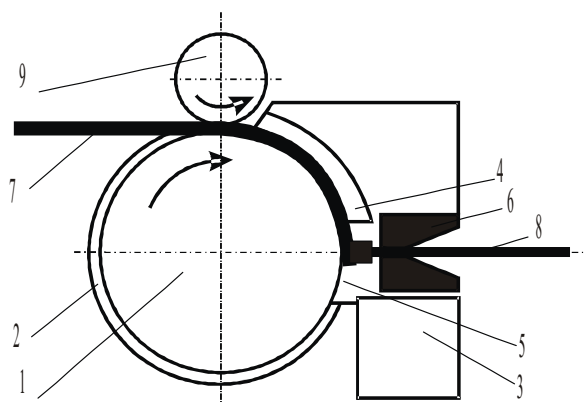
Схема процесу безперервного пресування по способу Конформ: 1 - робоче колесо, 2 - кільцева канавка, 3 - черевик, 4 - кільцева вставка, 5- вставка, 6 - матриця, 7 - заготовка, 8 - виріб, 9 - валок
